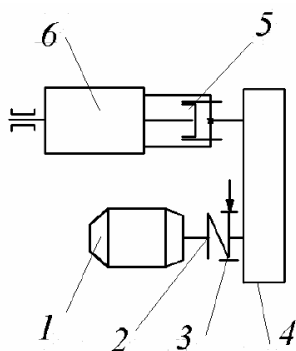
Кинематическая схема грузовой лебёдки: 1 – электродвигатель, 2 – упругая муфта, 3 – тормоз, 4 – цилиндрический редуктор, 5 – зубчатая муфта, 6 – грузовой барабан
